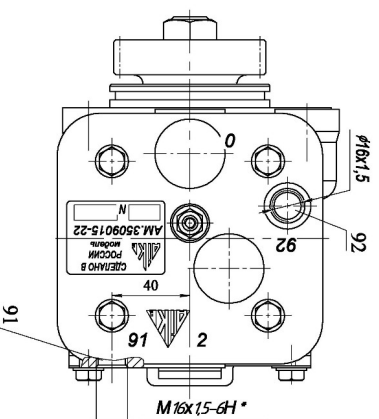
Присоединительные и установочные размеры компрессора АМ.3509015-12.
